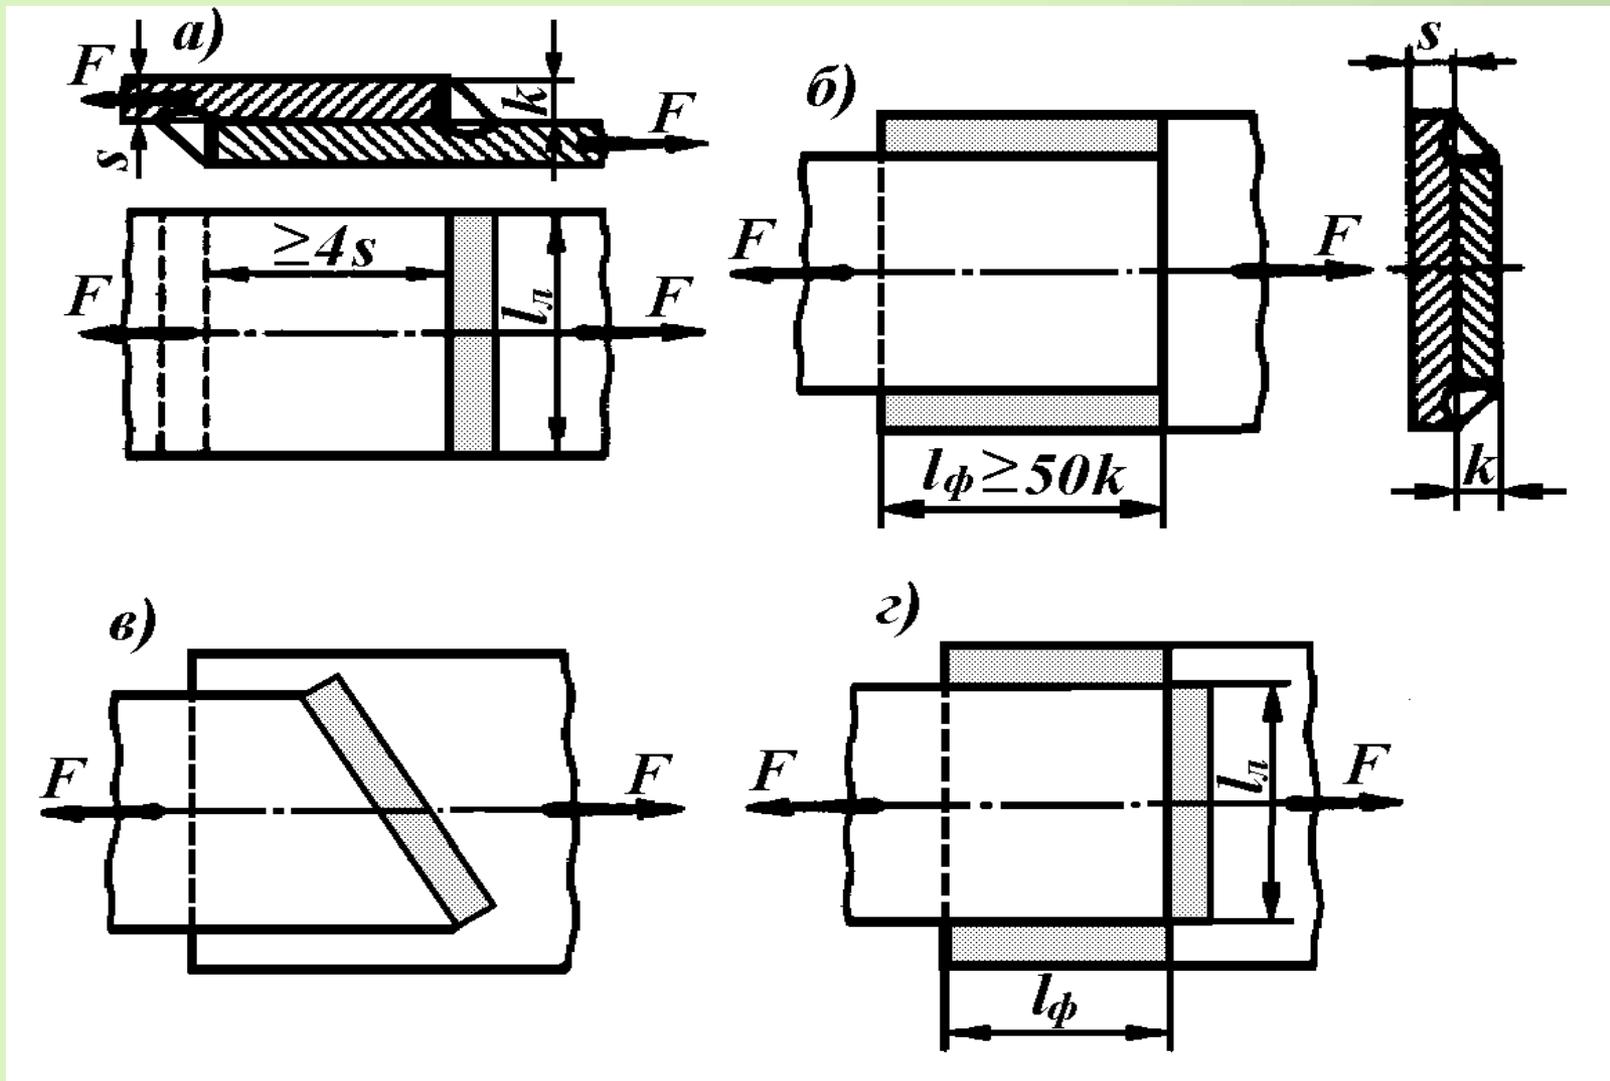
Расположение сварочных швов по отношению к действующей нагрузке: а) лобовой; б) фланговый; в) косой; г) комбинированный
